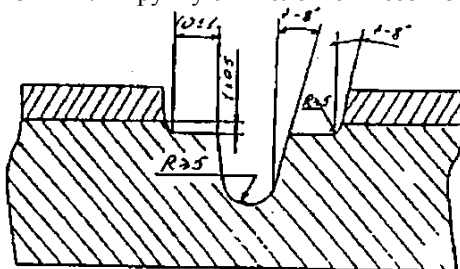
Подготовка кромок под сварку раздела основного и плакирующего слоя
